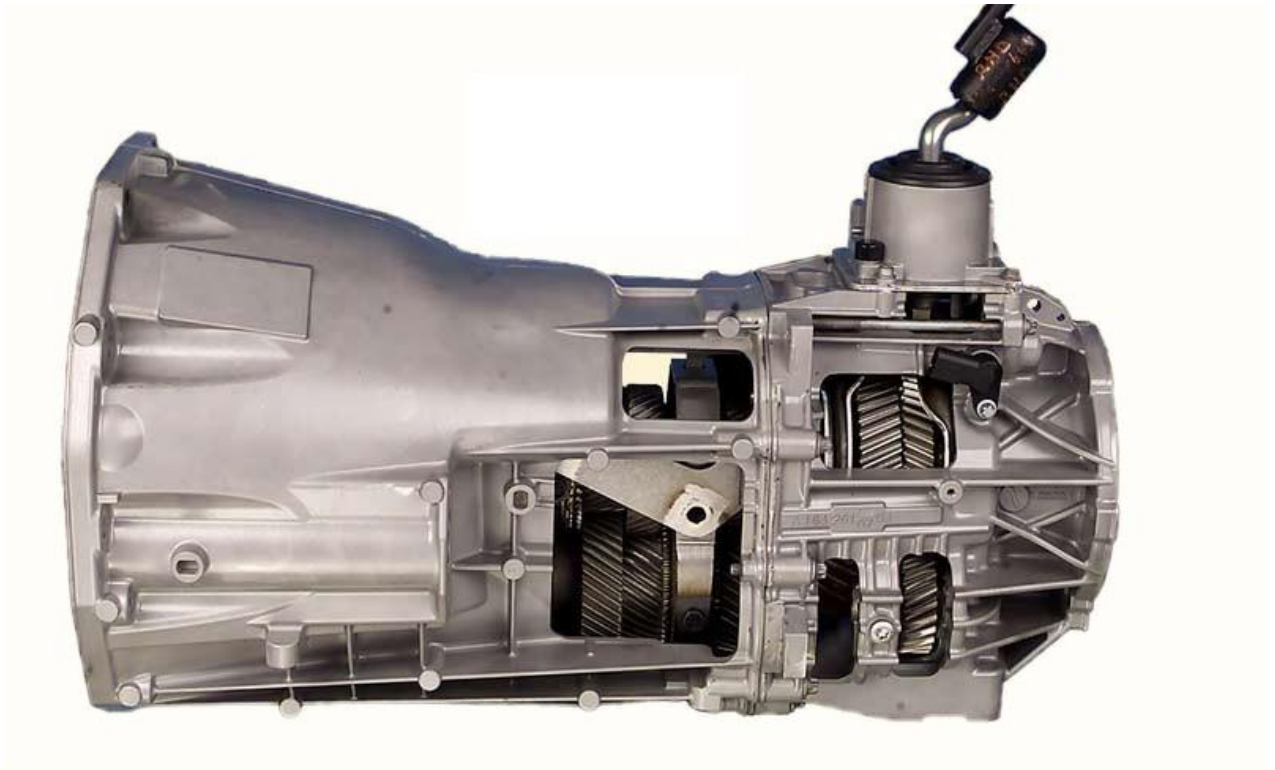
Коробка передач NSG370 автомобиля Jeep Wrangler TJ.
